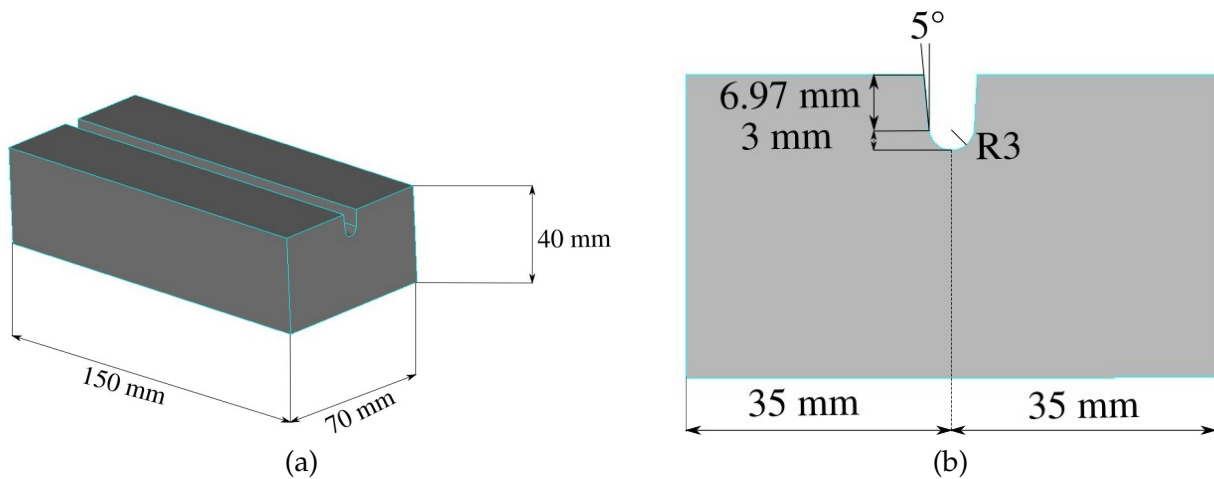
Dimensions de la maquette, (a) dimension de la plaque soudée, (b) dimensions du chanfrein étroit.
